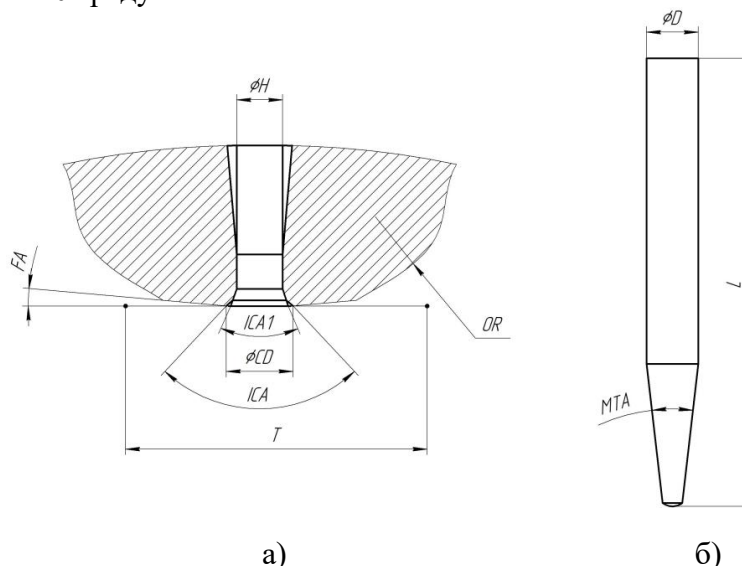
Рабочий торец микросварочного капилляра (а) и его общий вид (б)
